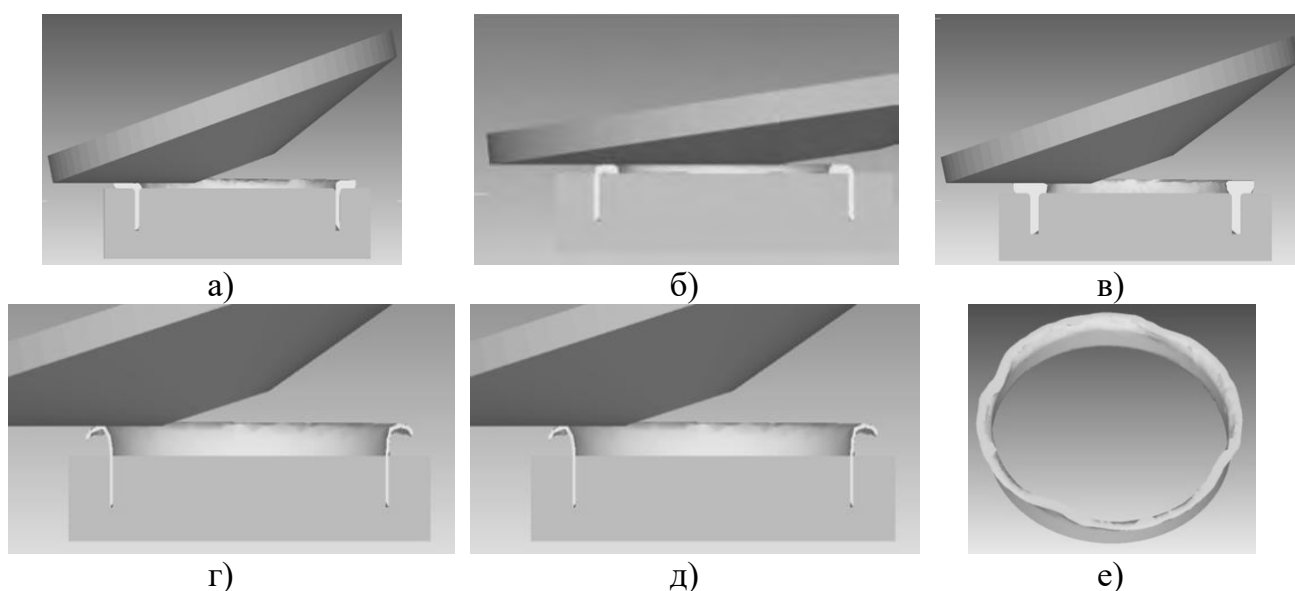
Виды формоизменения трубной заготовки при торцевой раскатке: а – образование наружного фланца; б – образование внутреннего фланца; в – осадка стенки заготовки с течением металла внутрь и наружу; г – потеря устойчивости заготовки с выворотом наружу; д – потеря устойчивости заготовки с выворотом внутрь; е - периодическая потеря устойчивости
